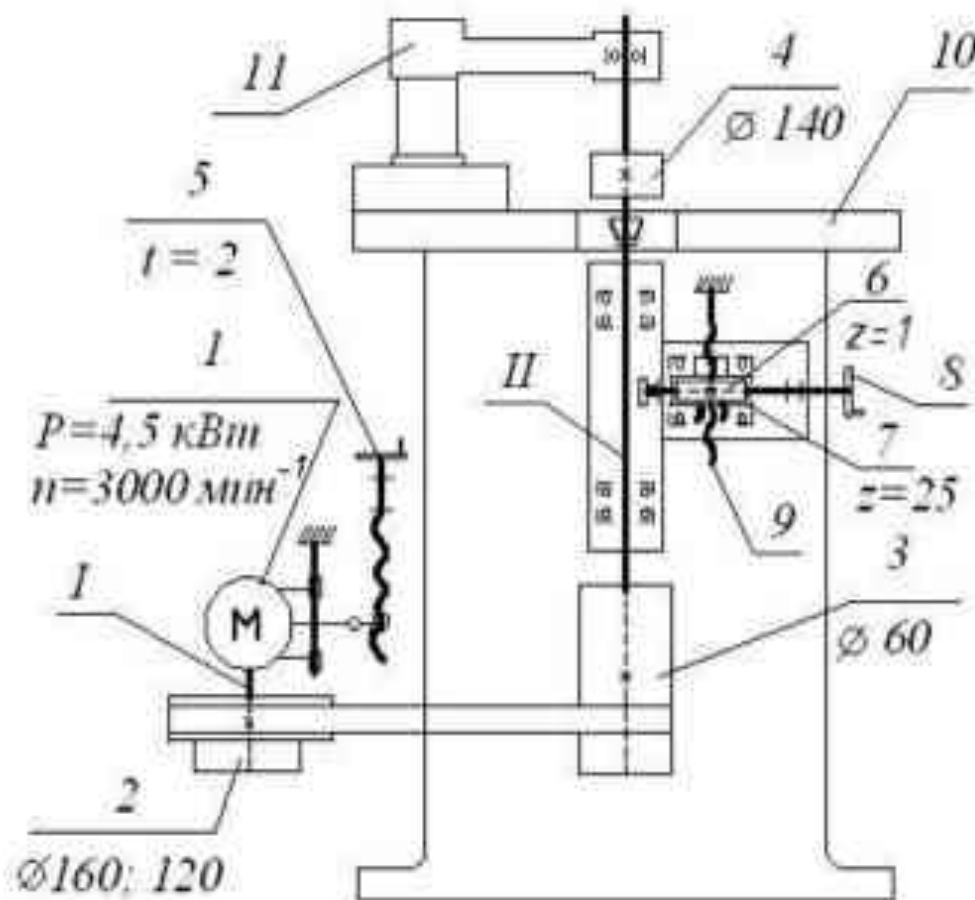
Кинематическая схема фрезерного станка Ф4
